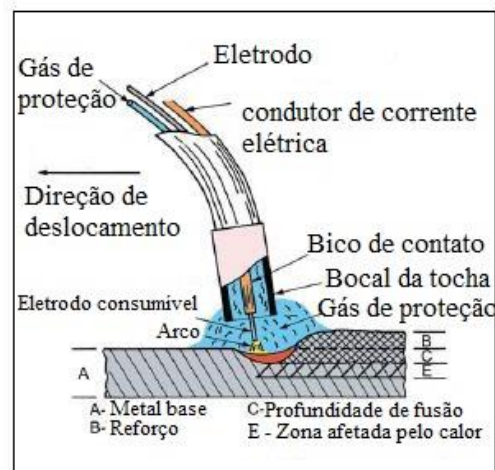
Vista geral do processo de soldagem MAG [Adaptado de AWS, apud Linnert, 2001].
